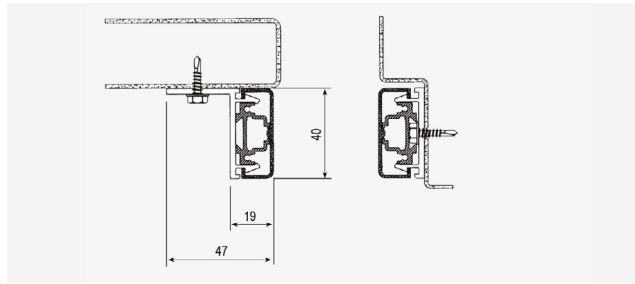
E40 - Ouverture latérale des portes (utiliser le support en L pour fixation sur la porte et le support plat pour fixation sur la colonne d'entrée)
